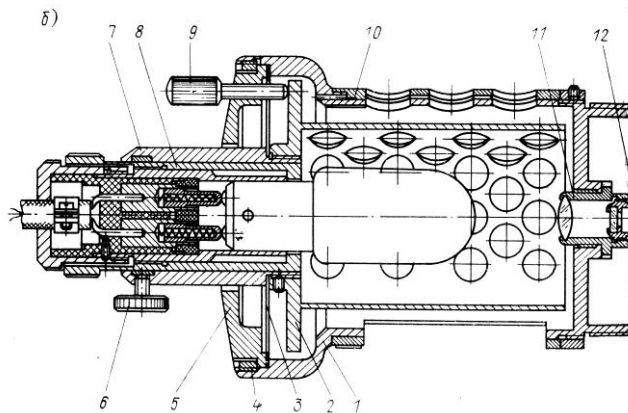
Конструкція освітлювача з лампою PH8-20: 1 – корпус; 2 – шайба; 3 – мембрана; 4 – різьбове кільце; 5 – кришка; 6 – гвинт; 7 – оправа; 8 – втулка; 9 – юстувальний гвинт; 10 – кожух; 11 – оправа лінзи; 12 – втулка
